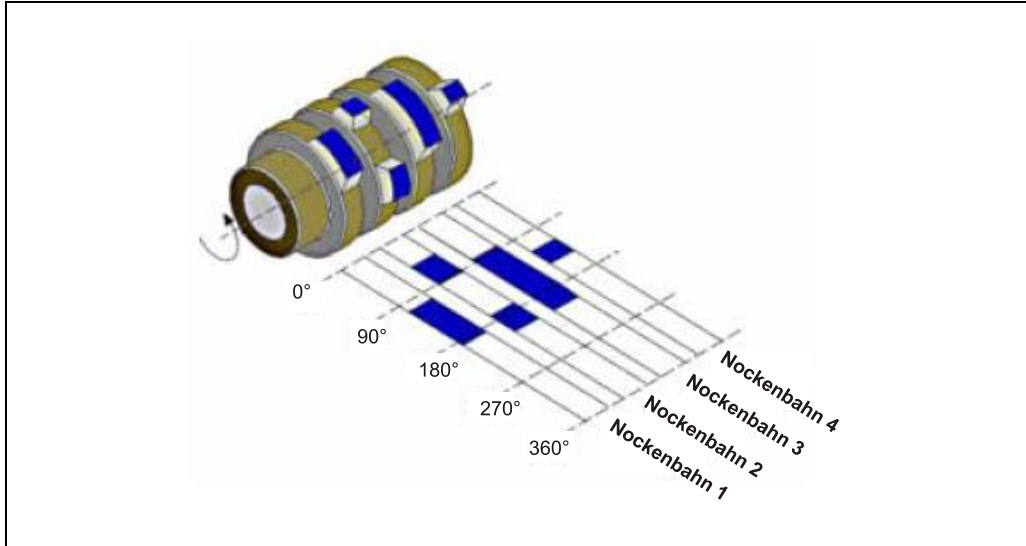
Beispiel für Mechanische Nockenscheibe mit vier Nockenbahnen
